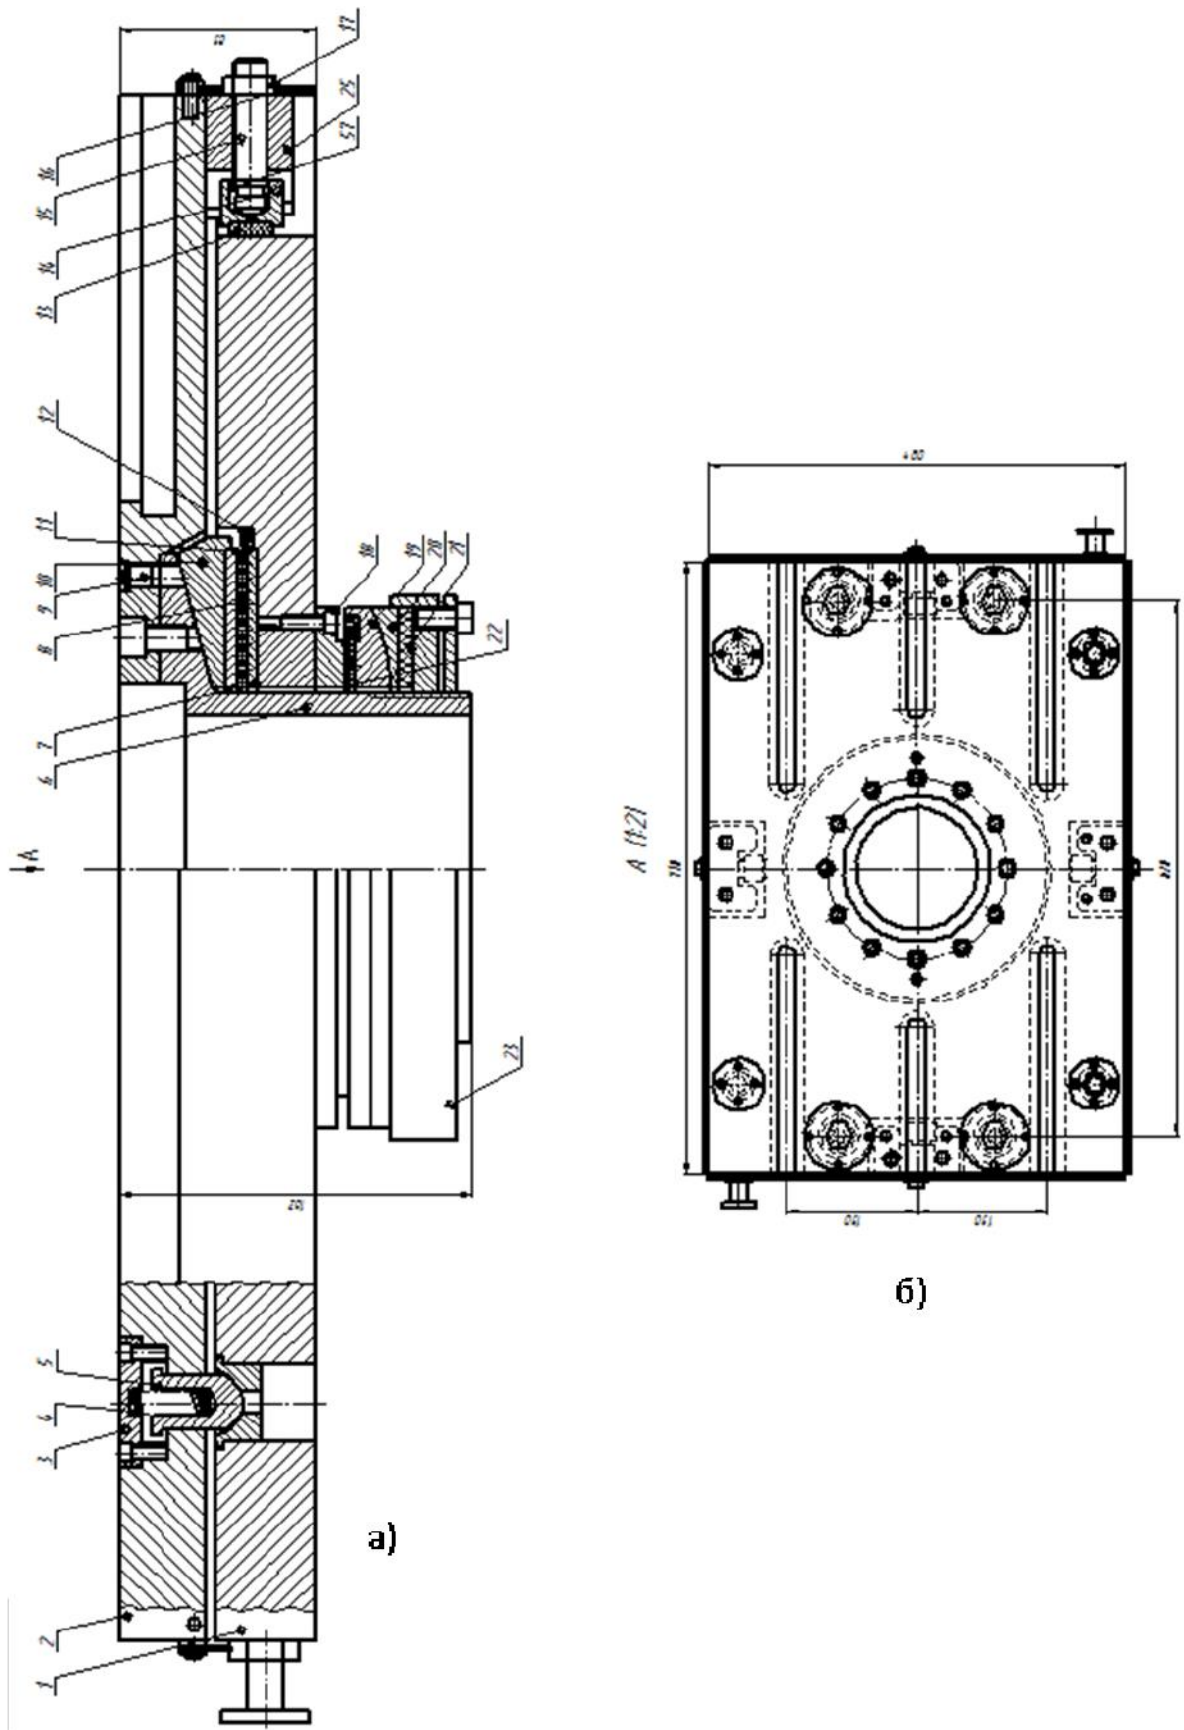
Робоча двовимірна схема компенсатора похибок відкритого кривошипного преса зусиллям 0,63 МН: а) – головний вид (повернуто); б) – вид в плані на верхню плиту;
